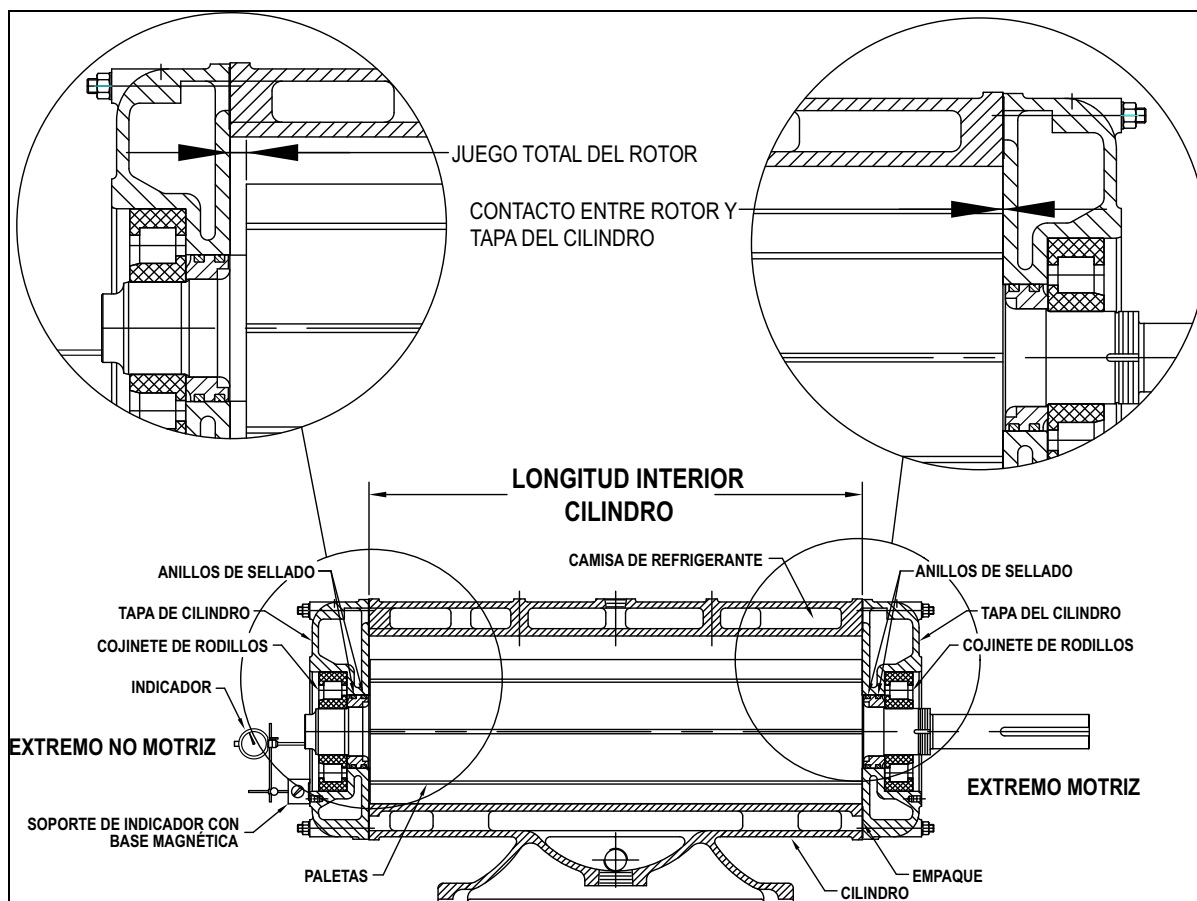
Juego total del rotor (cojinetes no posicionados por laines ni cubierta de extremo o adaptador del sello).
